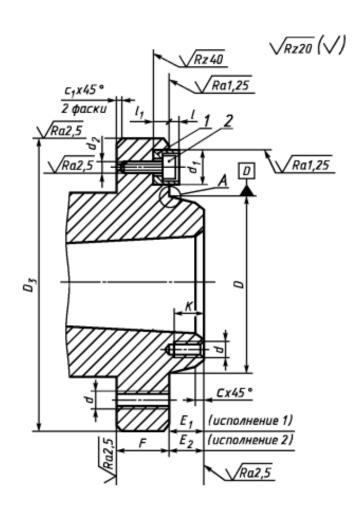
Присоединительные поверхности фланца шпинделя
